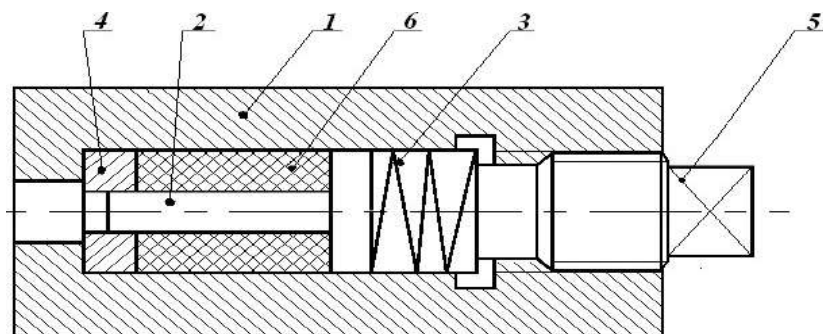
Пристрій для термообробки заготовок ПКМ в умовах всебічного стиснення:
